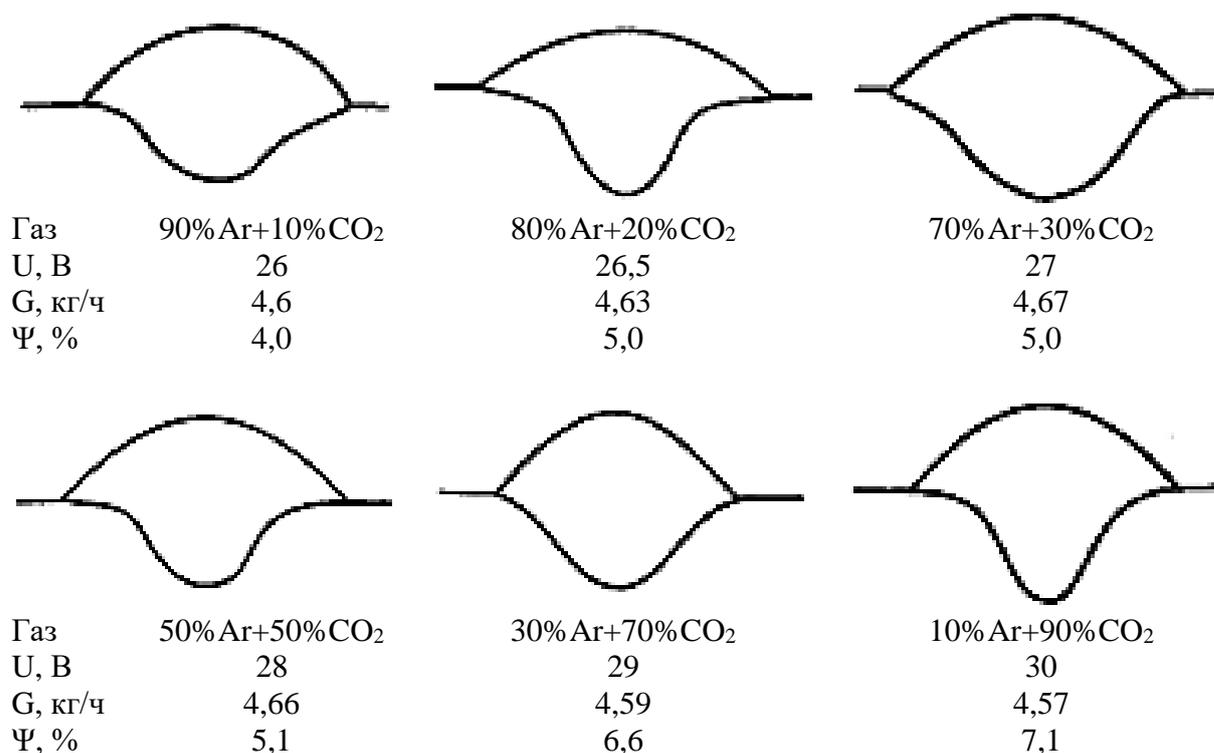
Изображенные профили сечения сварных швов, производительность плавления и уровень разбрызгивания металла при сварке с использованием газовой смеси Ar + CO<sub>2</sub>, осуществляемой при оптимальном напряжении дуги
